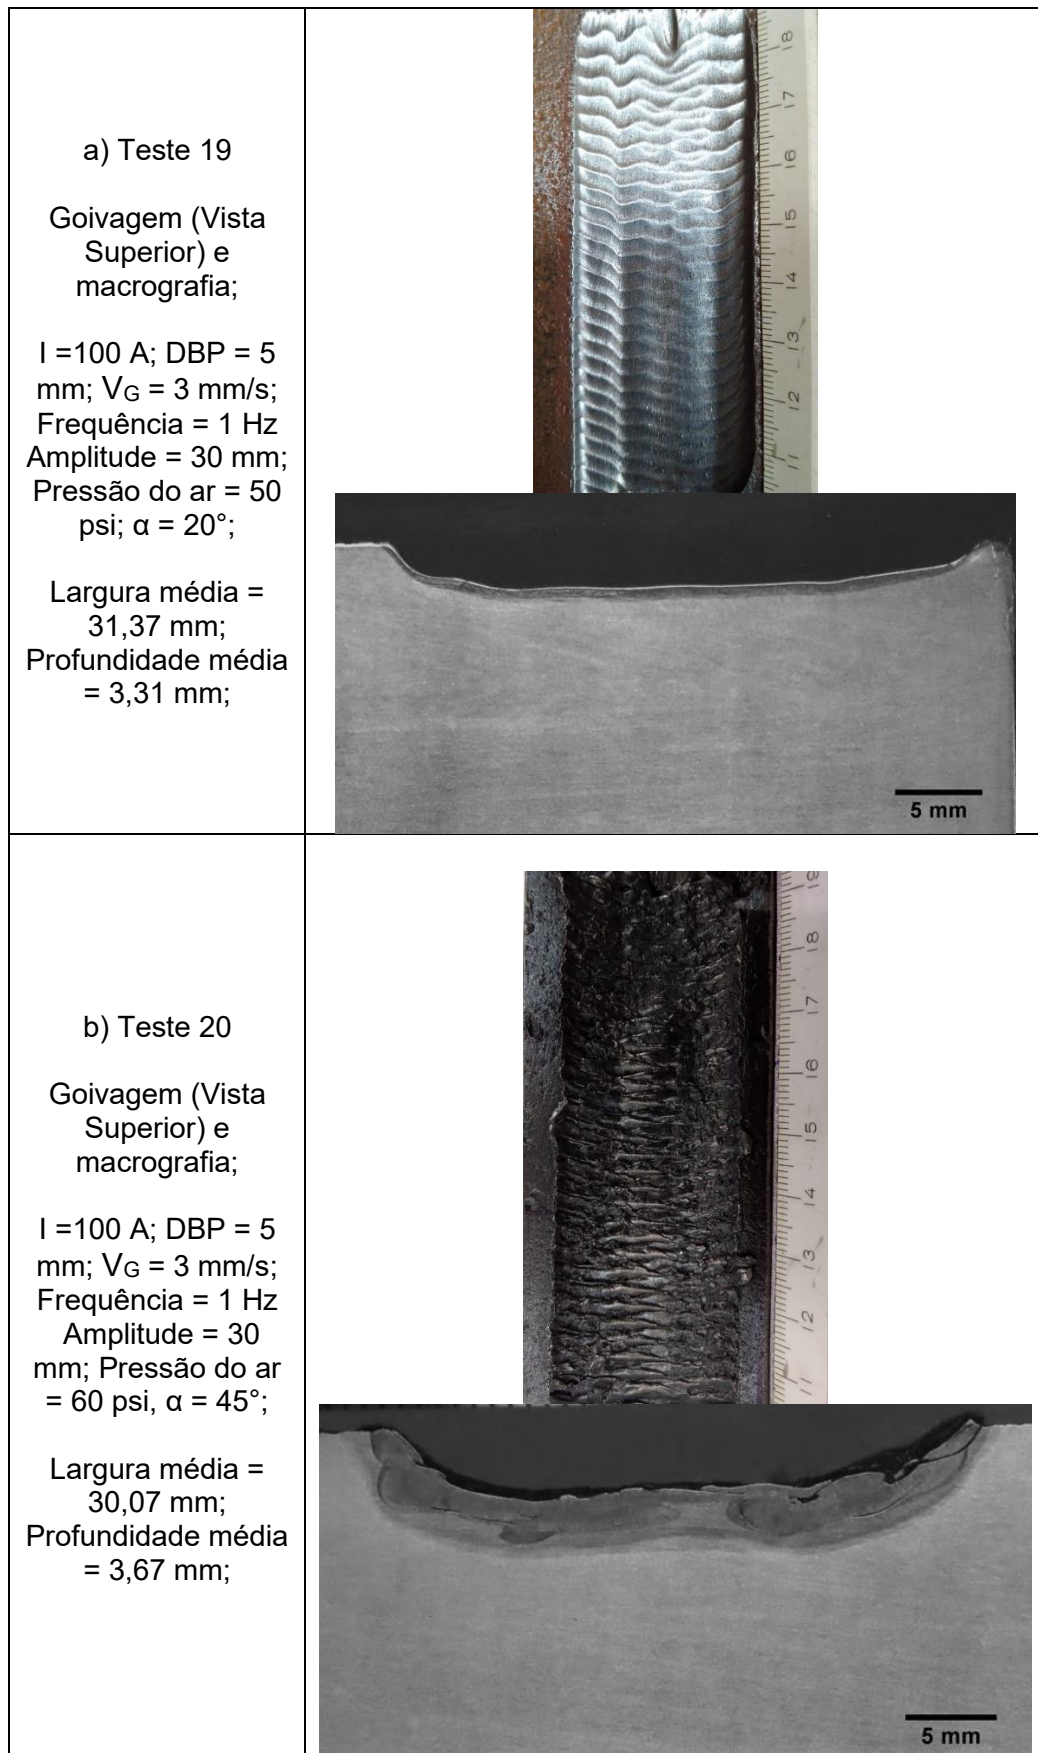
Testes 19 e 20 - Remoção com oscilação da tocha
